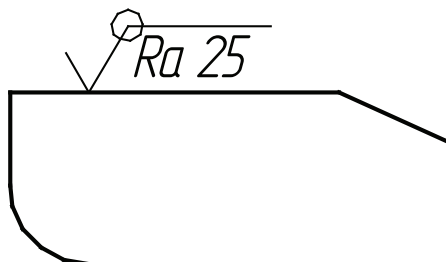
Обозначение шероховатости с одинаковым контуром
